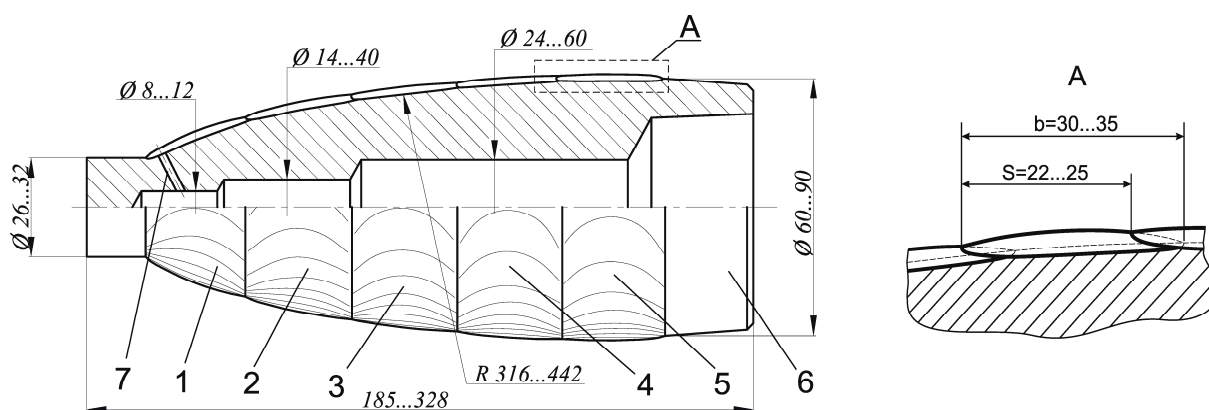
Схема формирования наплавленного металла на раскатной поверхности малогабаритных оправок: 1-5 – последовательно наплавливаемые валики наплавленного металла; 6 – оправка; 7 – каналы водяного охлаждения (после наплавки высверливаются).
